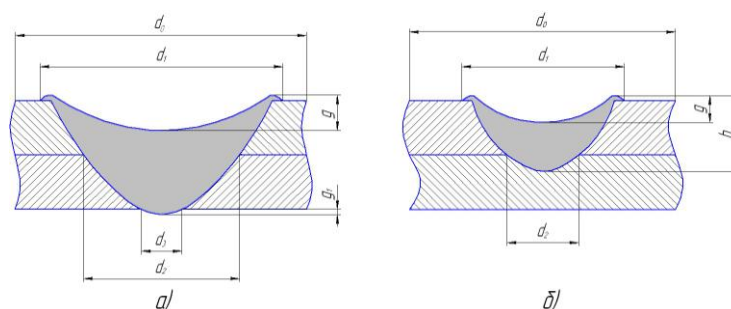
Сварка точками с полным проплавлением (а) и частичным проплавлением (б)
